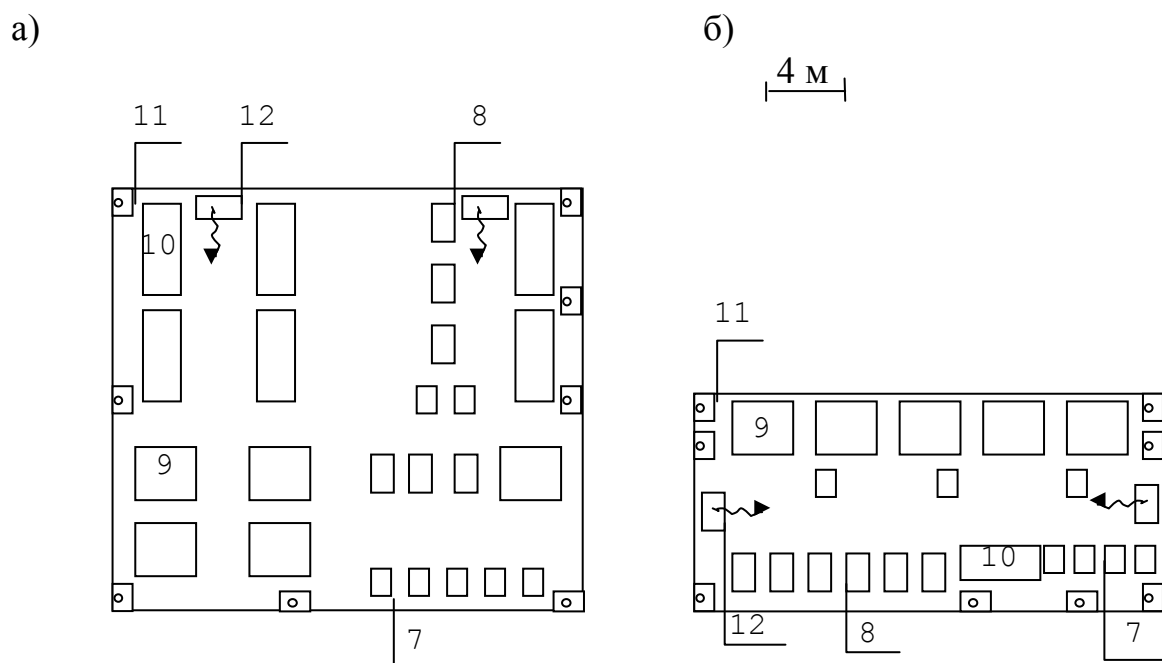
Расстановка оборудования сварочного участка
